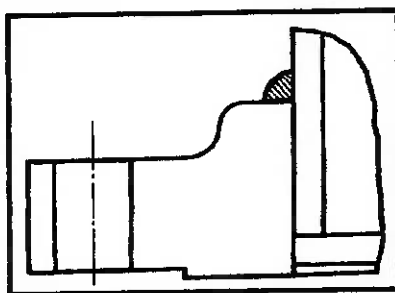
Posição de soldagem do filete externo do flange "Slip-On" ao pescoço da Boca de Visita
